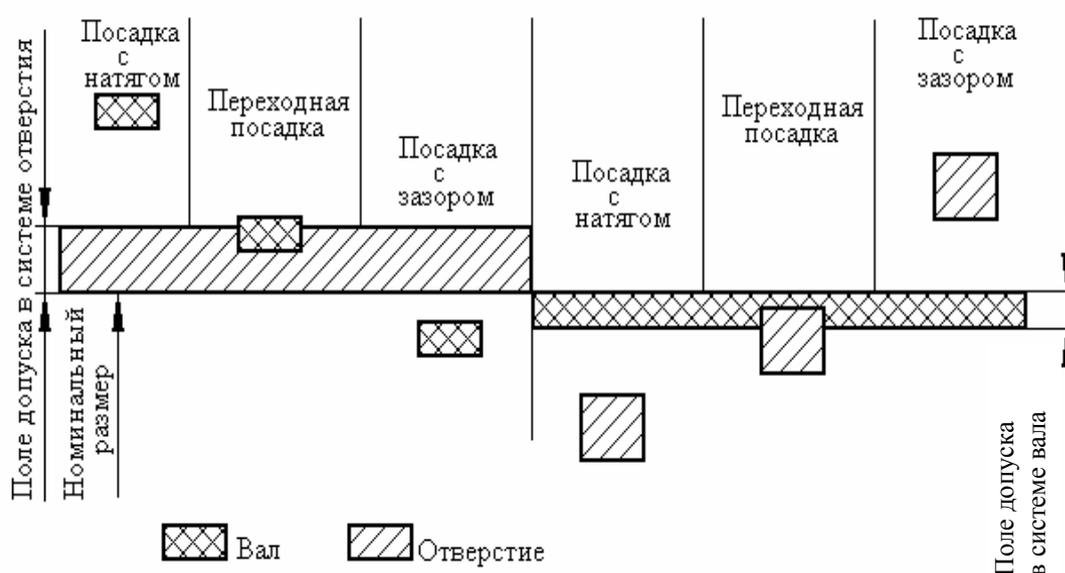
Поля допусков деталей в системе вала и в системе отверстия
